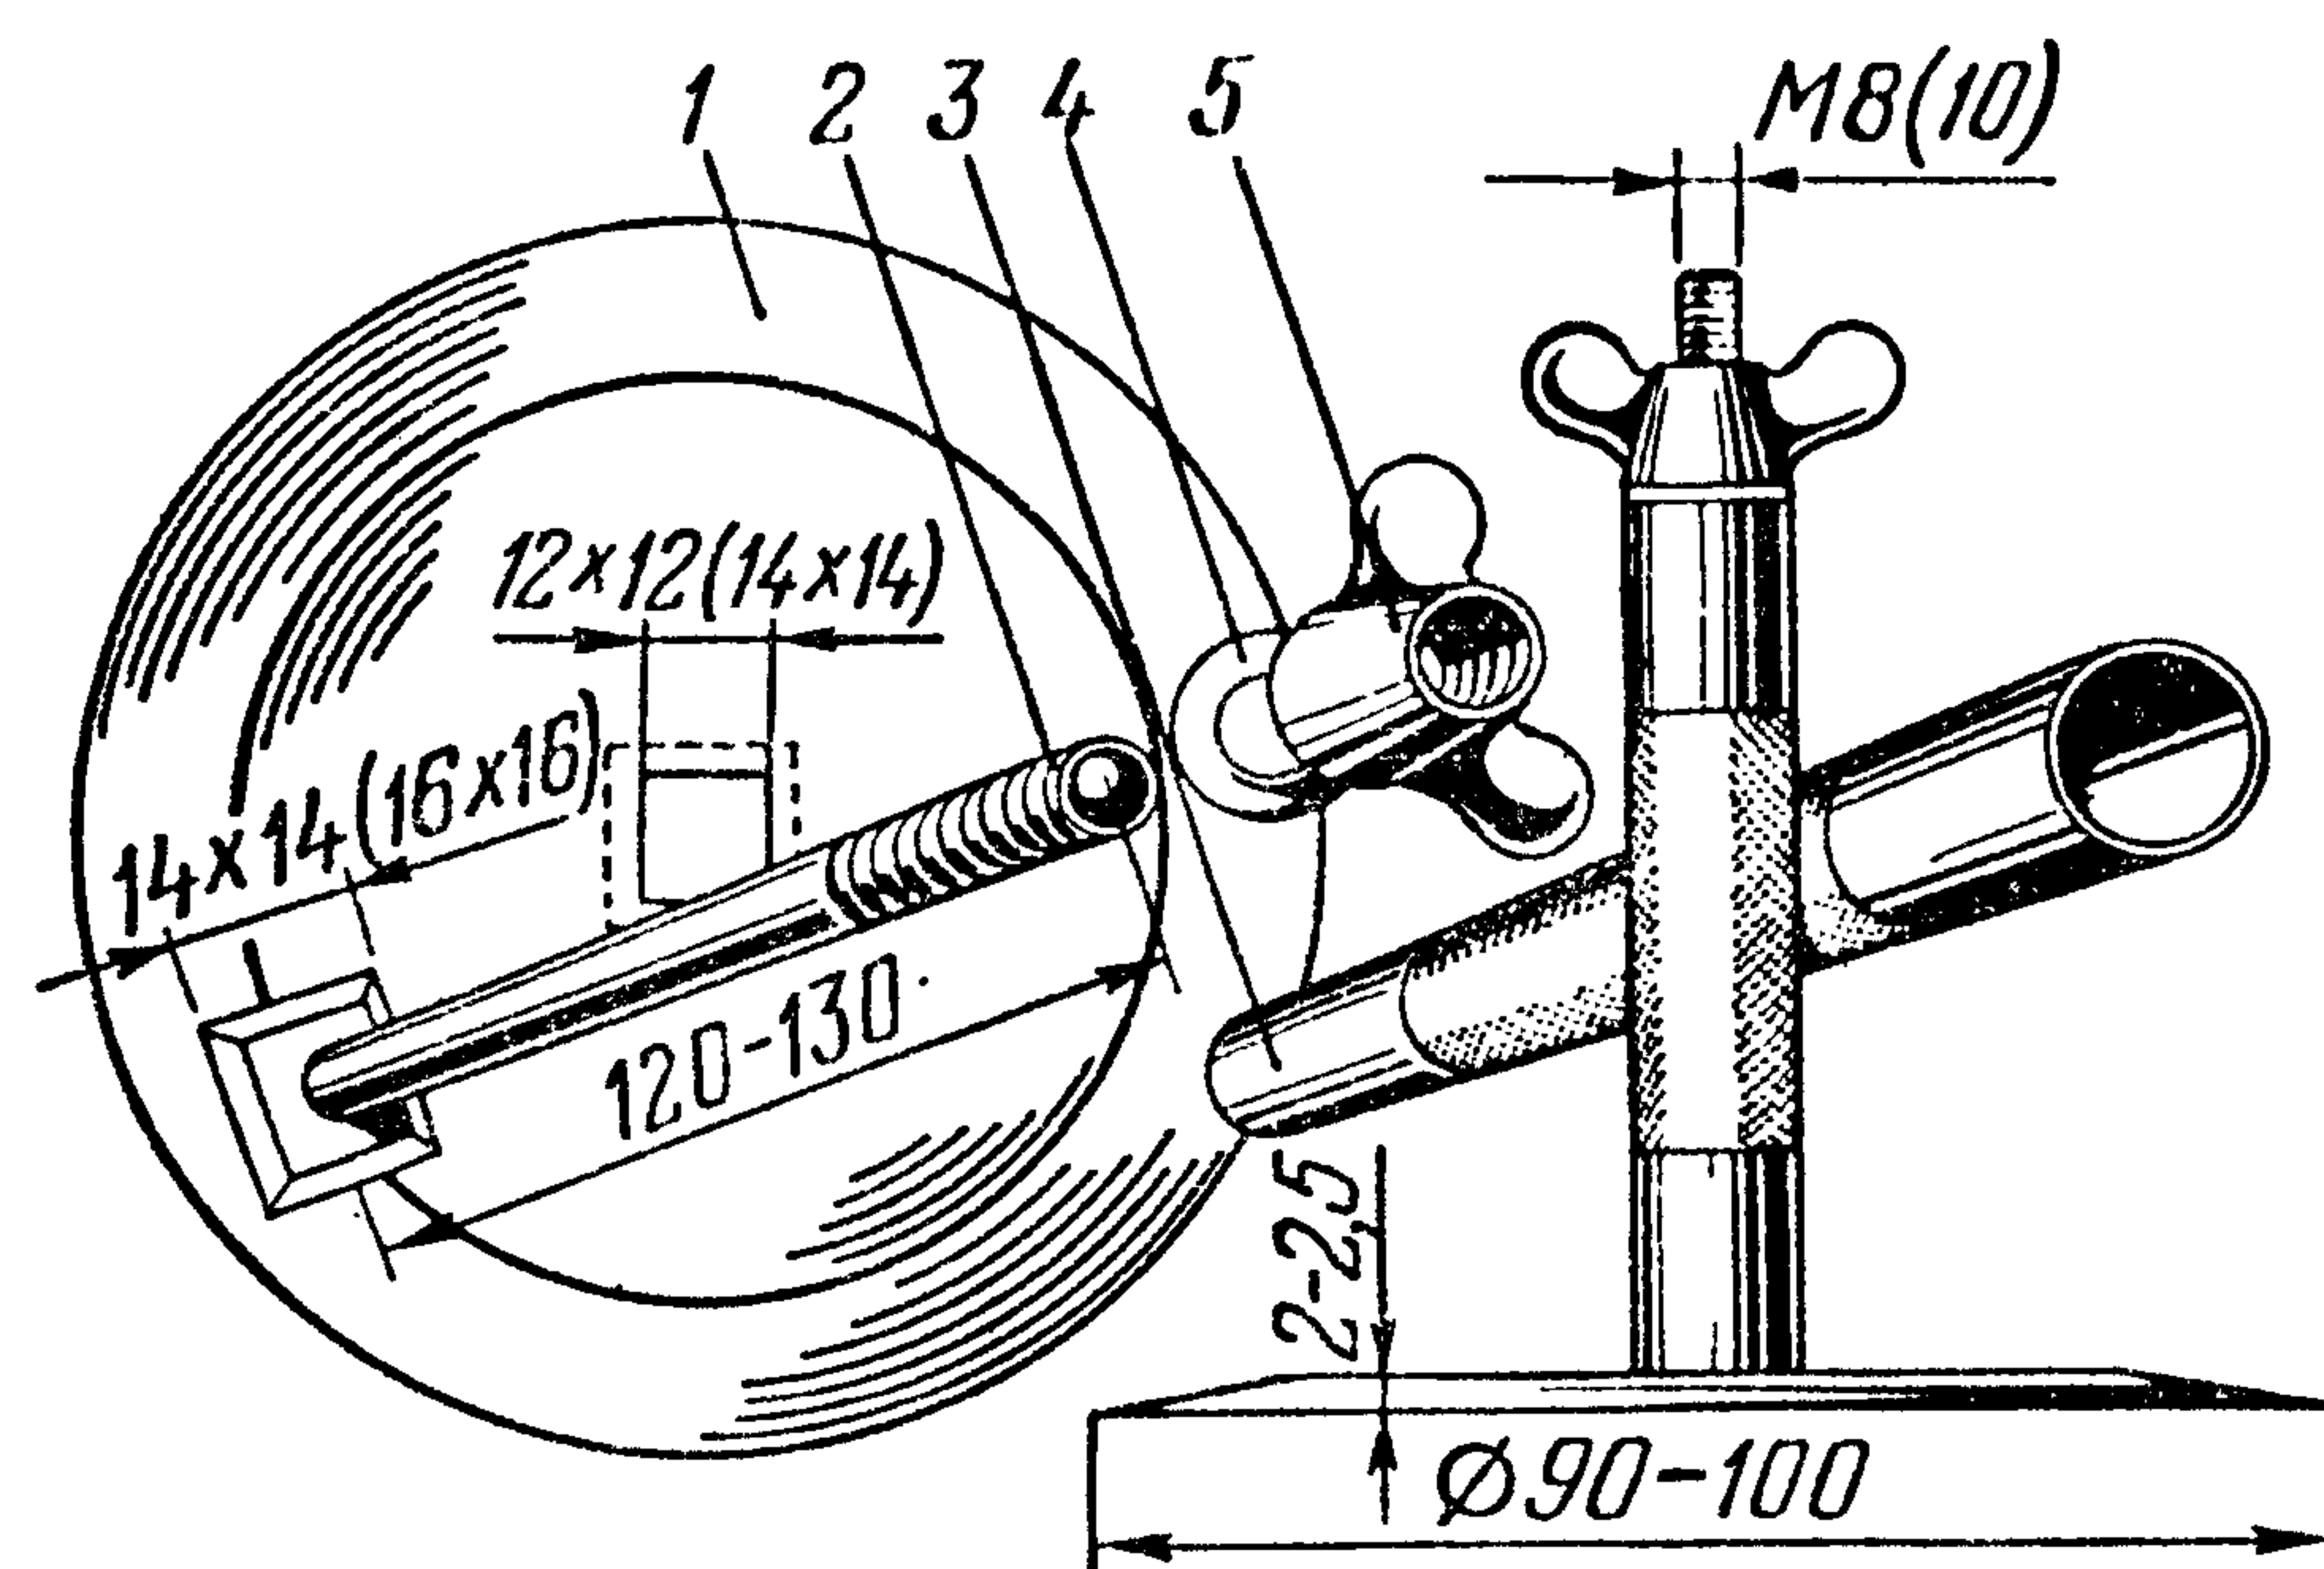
Дисковый нож: 1 — режущий диск; 2 — стержень-основание; 3 — рукоятка; 4 — шайба; 5 — гайка.
